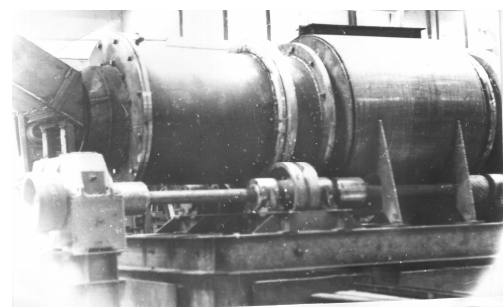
Установка для непрерывной отделочно-зачистной обработки деталей
